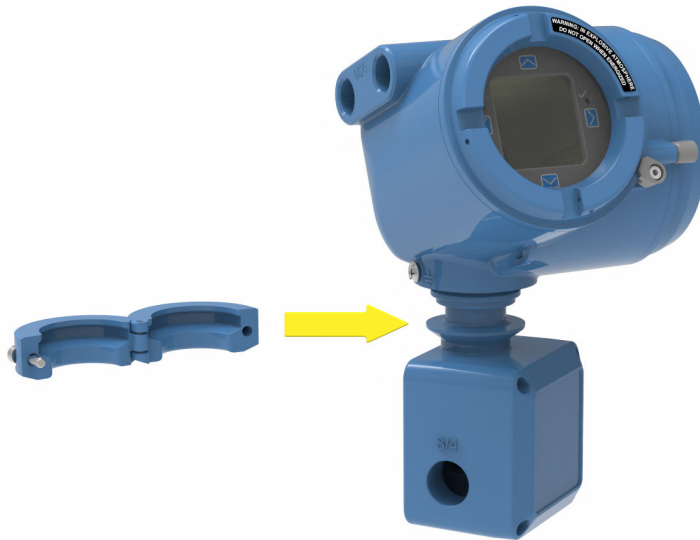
Rotación de la caja de conexiones del cableado del sensor
